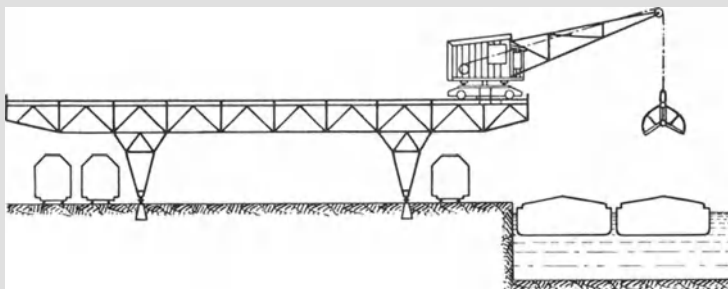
Verladebrücke mit fahrbarem Drehkran.
